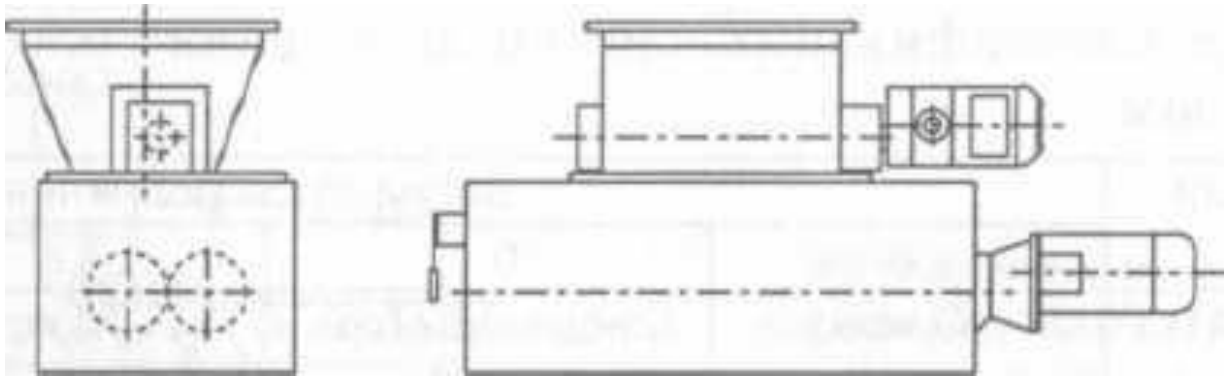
Двохвалкова дробарка для сухого подрібнення
